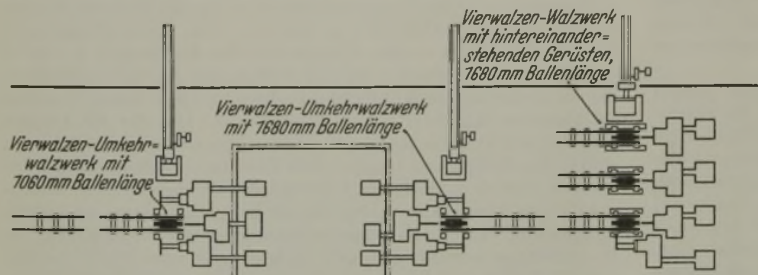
Kaltwalzwerksanlage mit zwei Vierwalzen-Umkehrwalzwerken und einer Walzenstraße mit hintereinanderstehenden Gerüsten.
